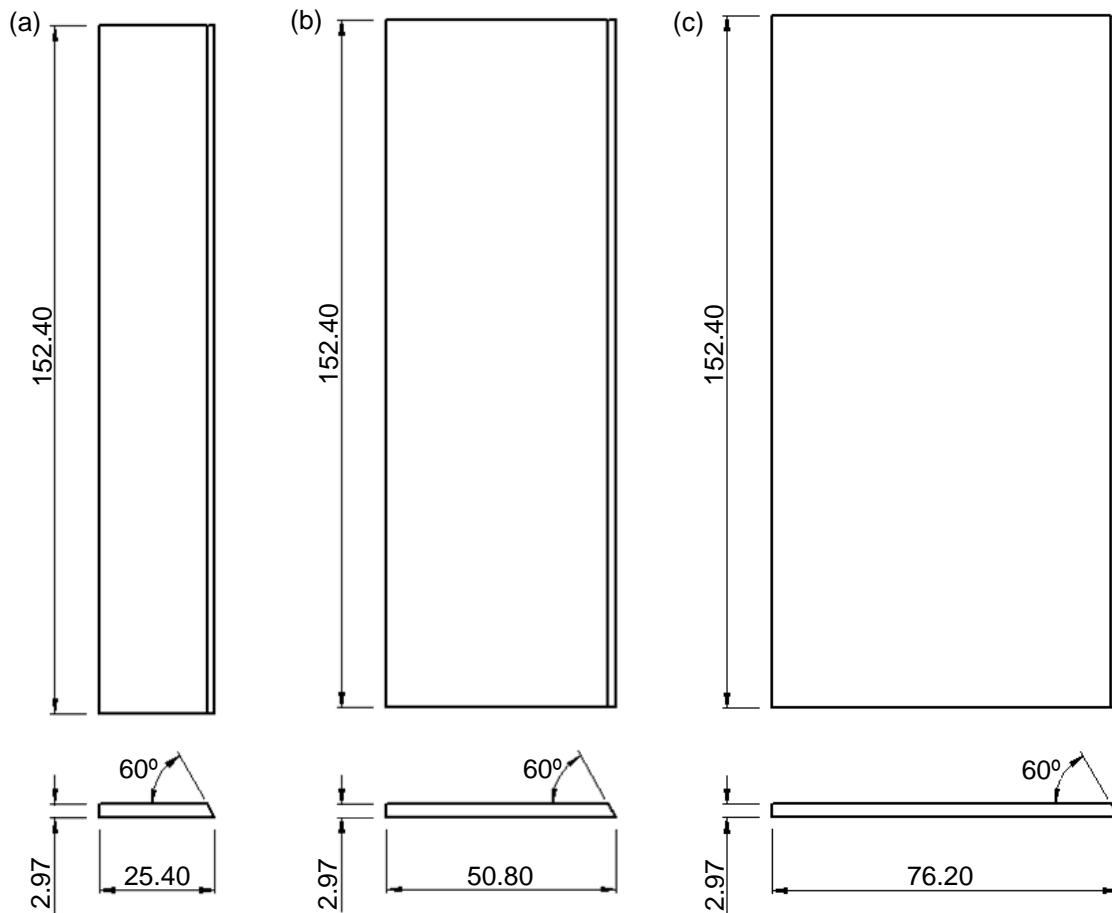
Vistas de las placas utilizadas para las juntas soldadas: (a) 25.40 mm, (b) 50.80 mm y (c) 76.20 mm.
